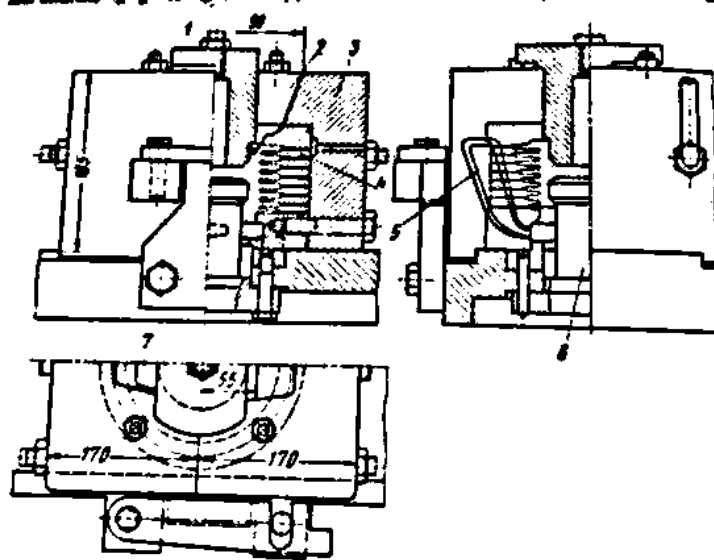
Кокіль для лиття біметалевих циліндрів [13]
